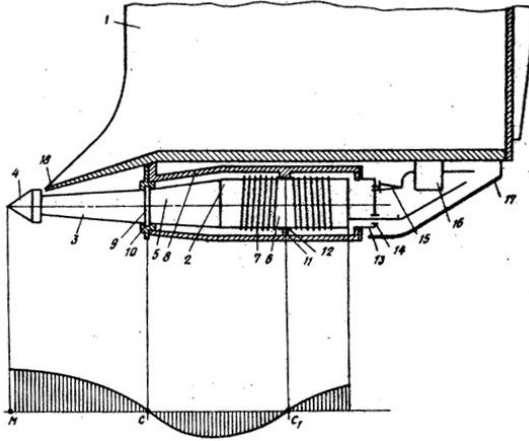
Ковш экскаватора с вибрирующими зубьями: 1 – ковш; 2 – вибратор (в сборе); 3 – магнестрикционный вибратор; 4 – зуб; 5 – волновод; 6 – сердечник; 7 – обмотка возбуждения; 8 – разъемный корпус; 9 – крепление; 10 – разъемная крышка; 11 – выступ; 12 – антифрикционные прокладки; 13 – крышка; 14 – разъем для ввода проводов обмотки возбуждения; 15 – штуцер для подвода охлаждающей жидкости; 16 – коллектор; 17 – оградительный кожух; 18 – козырек ковша
